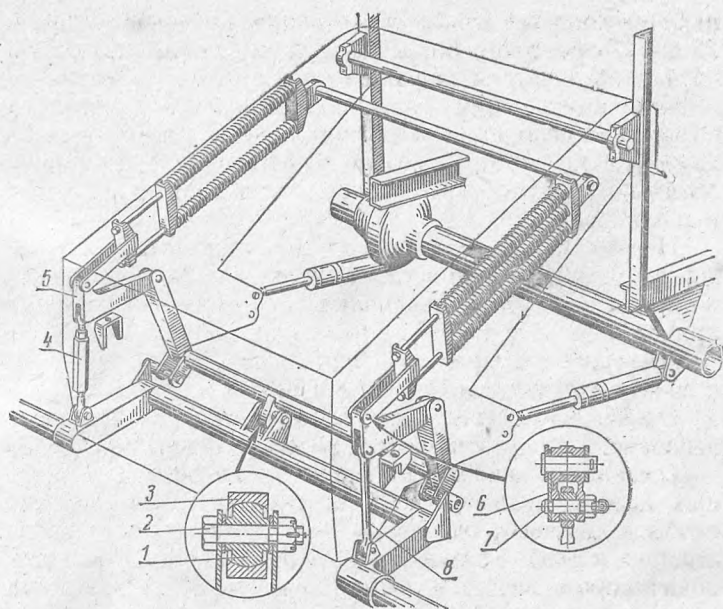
Схема подвески и уравнивания корпуса жатки:
